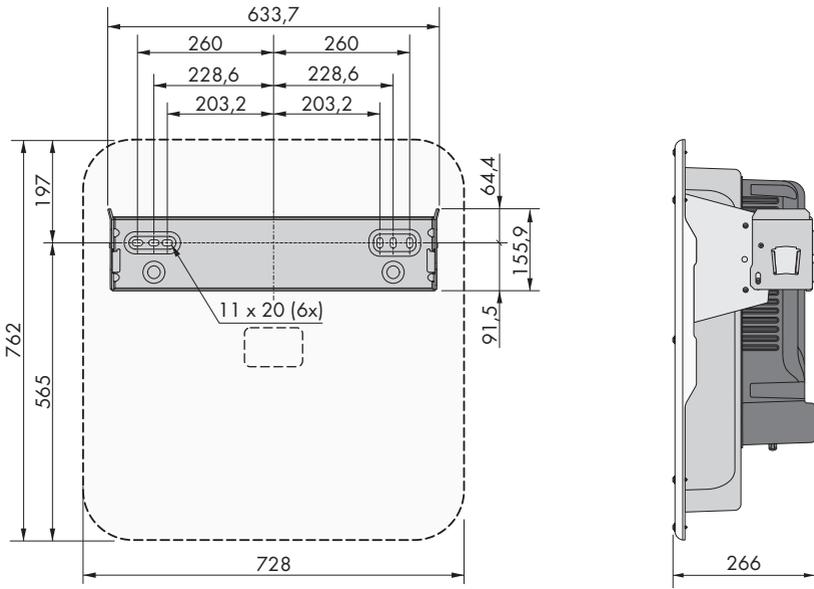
Posición de los puntos de fijación (Medidas en mm)
